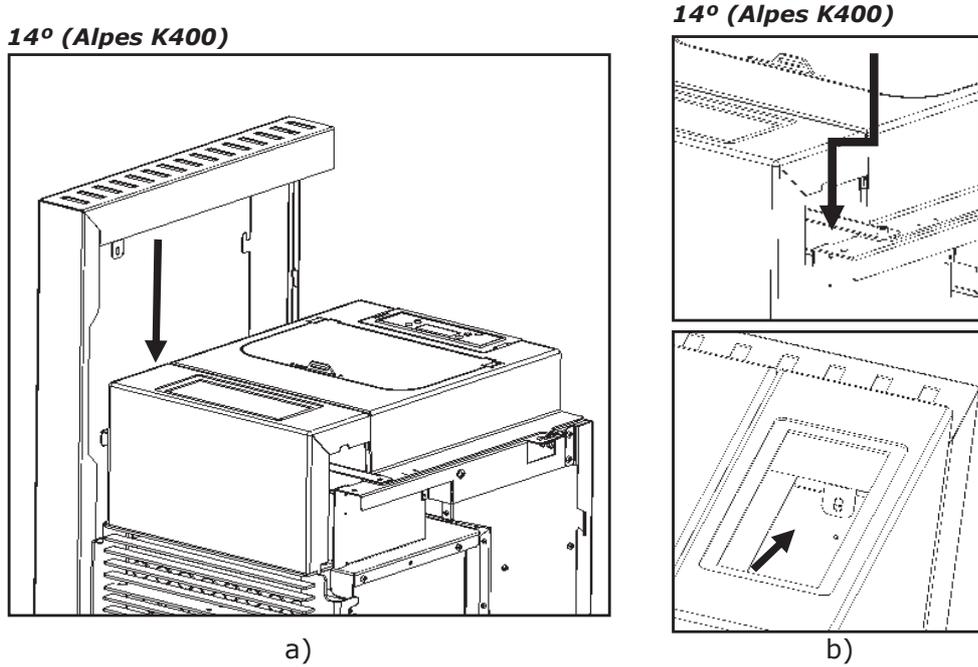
Encaje de las lengüetas en las estructuras laterales
